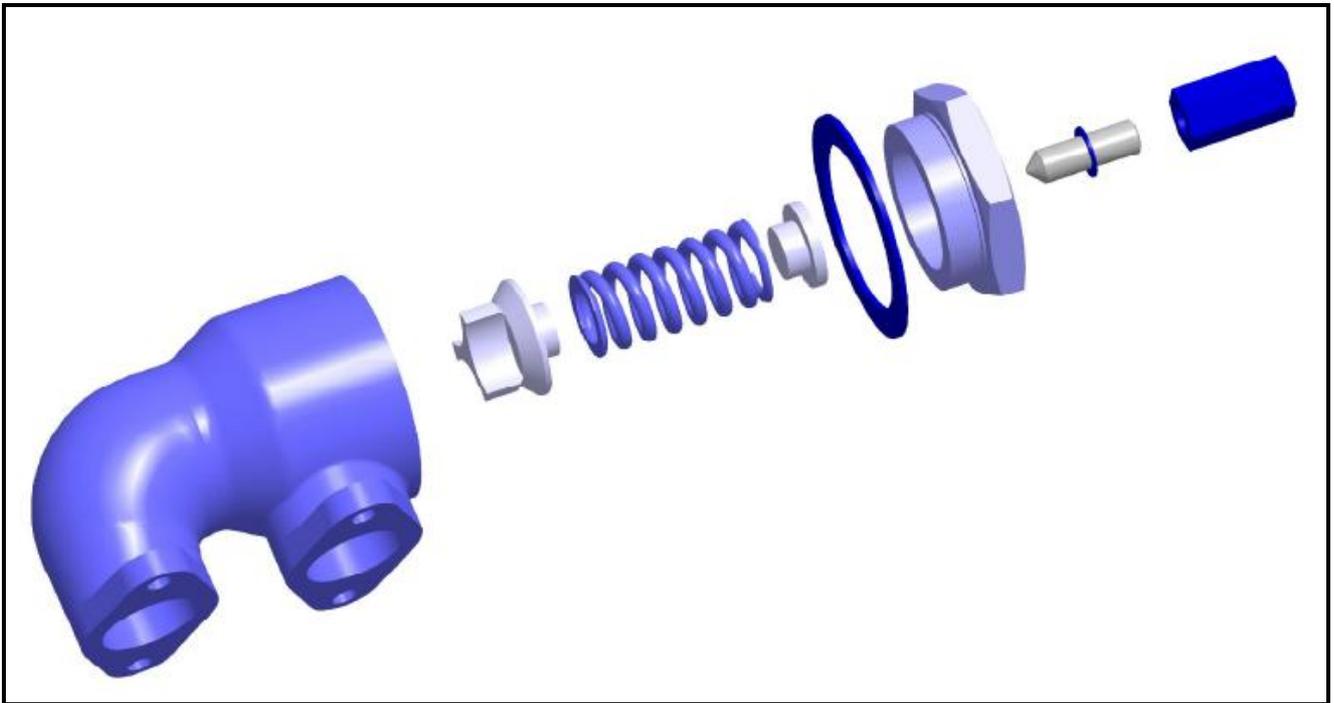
3D-Explosionsansicht - Sicherheitsventil
